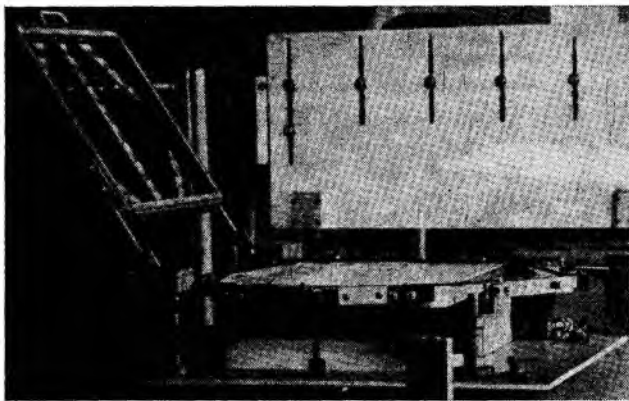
Резак-электрод для сварки ТВЧ
